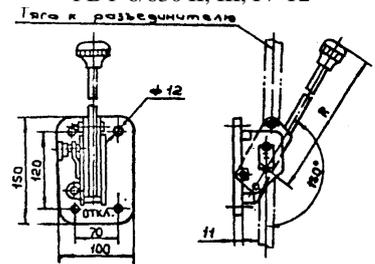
Привод рычажный типоразмера ПР-11А-I, II УХЛ2,
